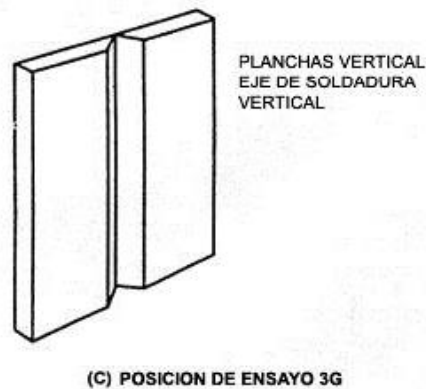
Posición de soldadura 3G, tabla D 1.1
